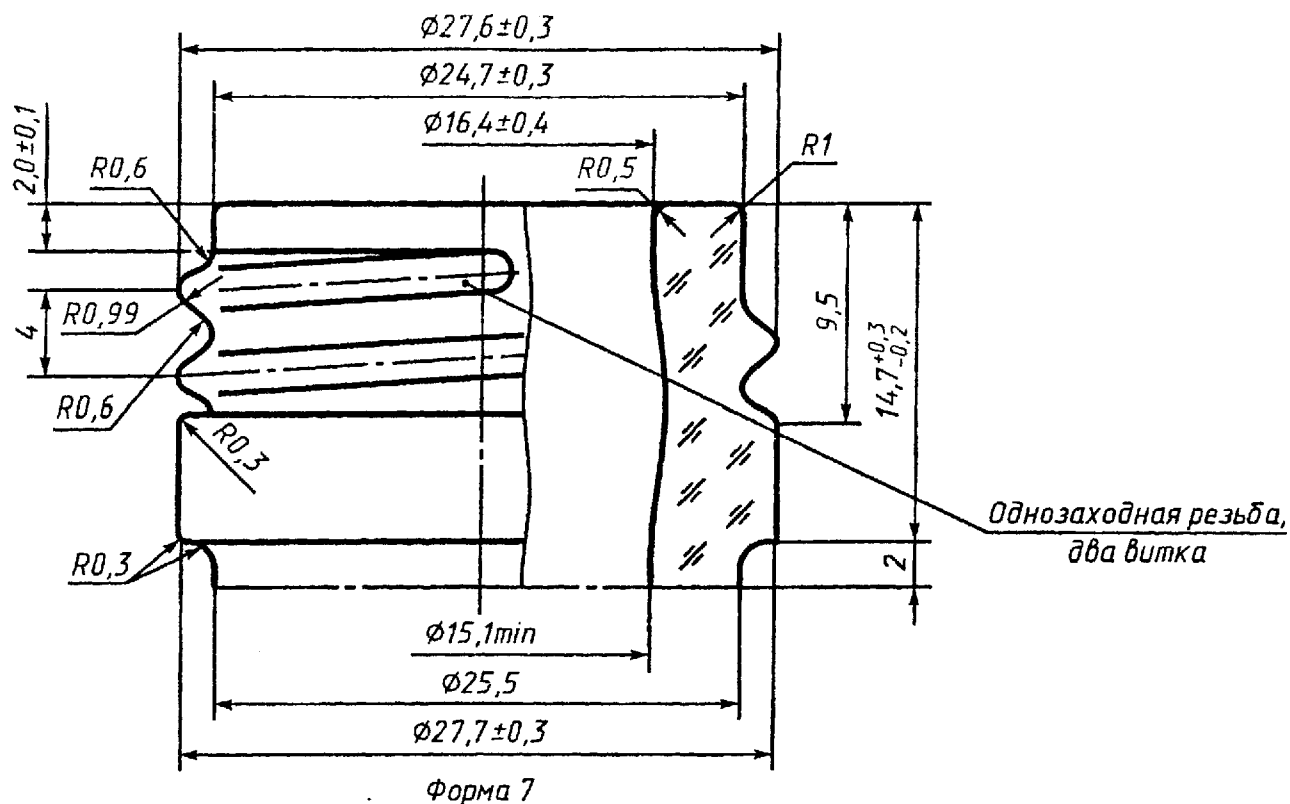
Детали конструкции винтовых венчиков горловин
